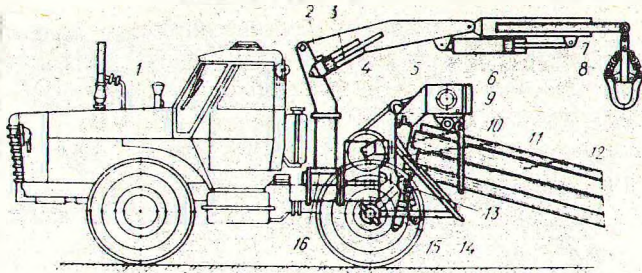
Машина для трелевки деревьев:1-шасси;2-манипулятор;3,6,8-гидроцилиндры;4-шарнир;5-откидная часть арки;7-захват;9-поперечная балка;10-арка;11-лебедка;12-пачка деревьев;13-гидроцилиндр.шита; 14-цит;15-гидроцилиндр арки;16-подрамник.
